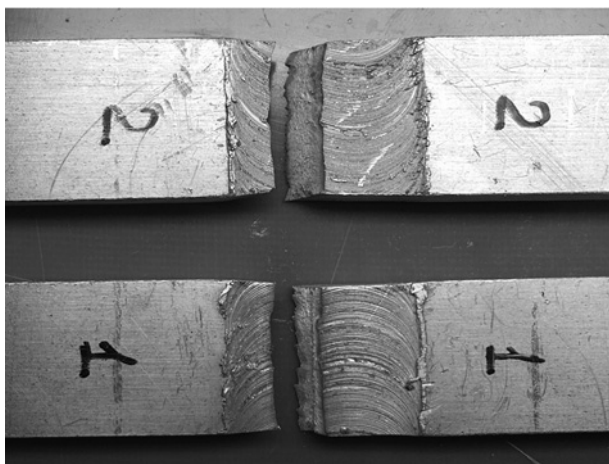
Образцы сварных соединений после испытаний на статическое растяжение
